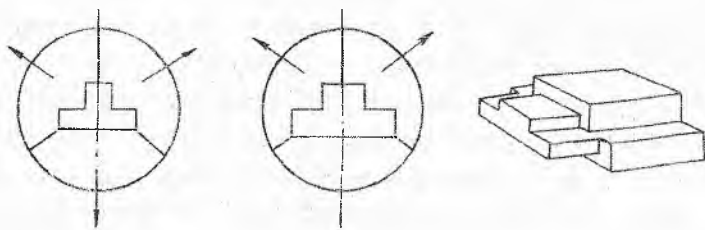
Конструкции разъемных матриц для прессования профилей с законцовками
